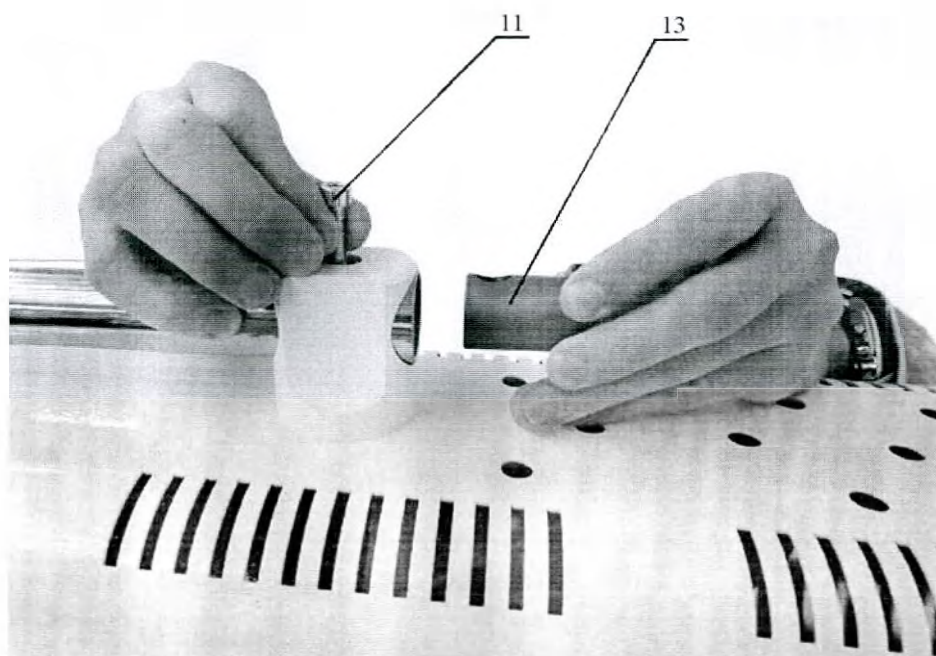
Вставка заглушки 13 в верхний торец трубы 2
